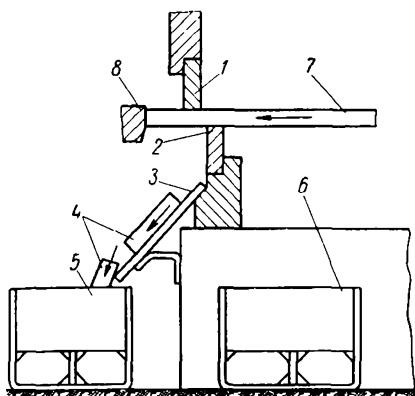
Схема уборки заготовок в тару: 1 — верхний нож; 2 — нижний нож; 3 — скат; 4 — заготовки; 5 — тара для заготовок; 6 — тара для остатков; 7 — штанга; 8 — упор
